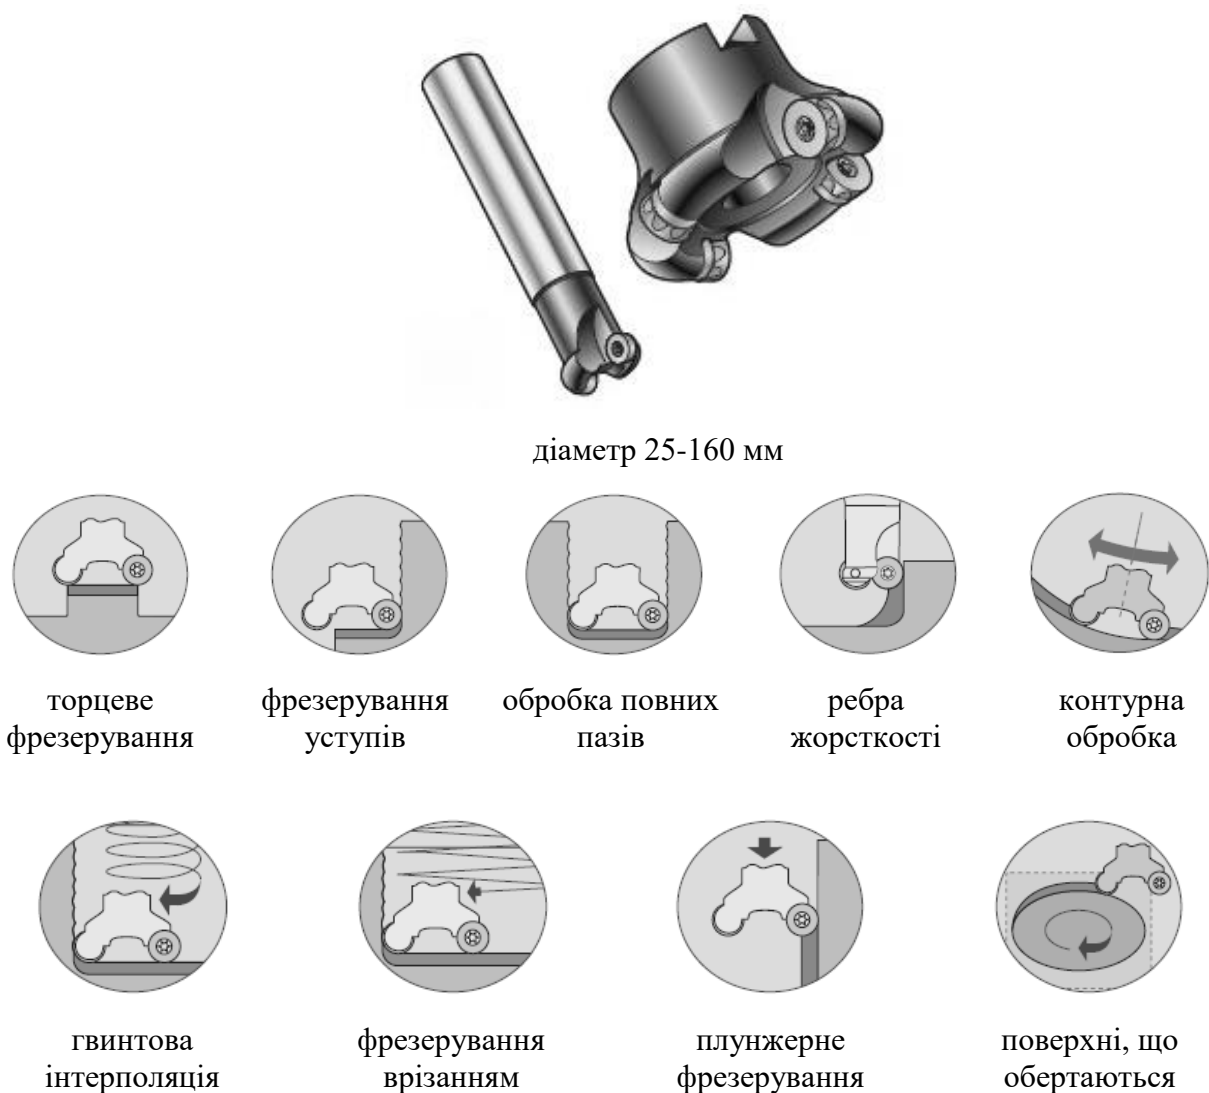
Основні технологічні операції, що здійснюються фрезами з круглими ріжучими пластинками для торцевого фрезерування у важких умовах, торцевого фрезерування і обробки профілів
